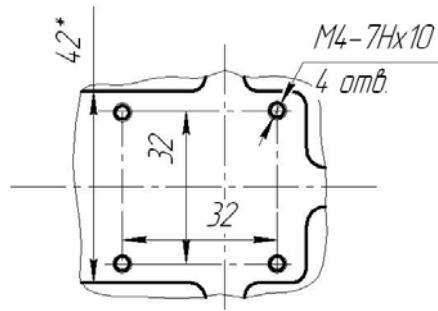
Присоединительные размеры под установку датчиков вибрации
